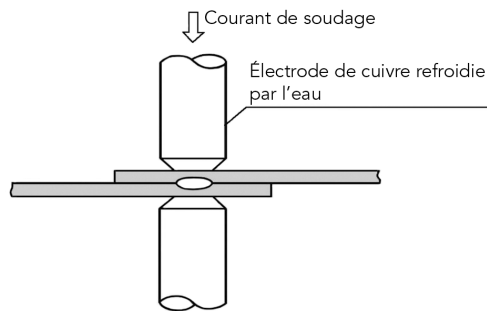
Principe du soudage électrique par résistance par points.
